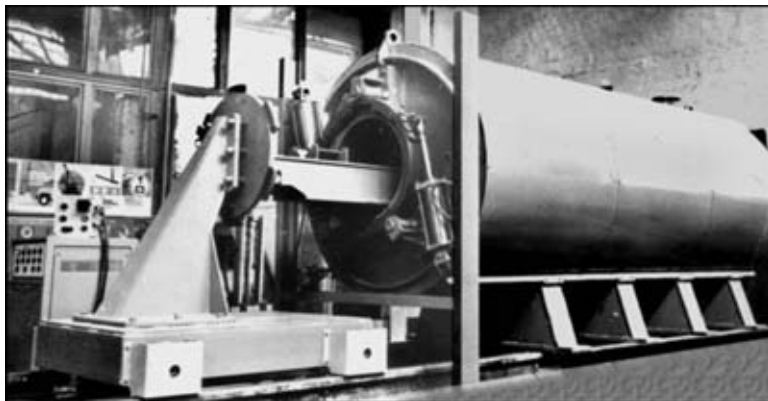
Установка ОБ2200 для сварки взрывом
